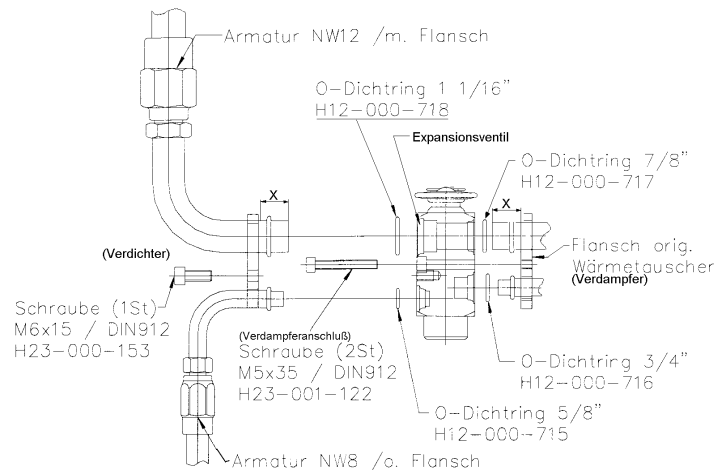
Füllventil - Lötadapter für R134a O-Ring - Anschlüsse
